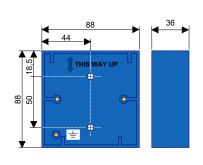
Montagegehäuse auf Putz (Art.-Nr. 704981) Fig. 7: Back box for surface mounting (Part No. 704981)
